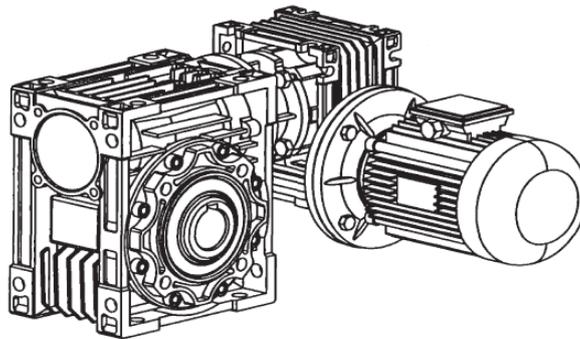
Двухступенчатый червячный мотор-редуктор фирмы *MOTOVARIO
